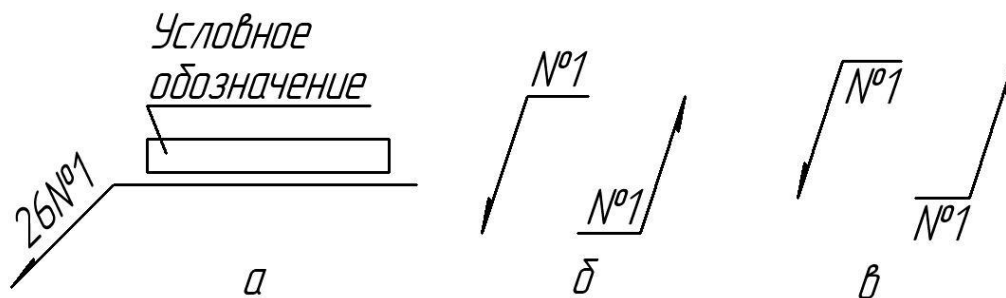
Обозначения сварных швов на чертеже
